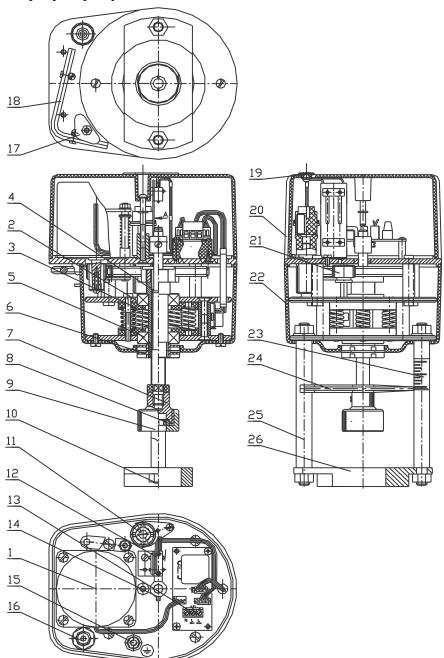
Устройство исполнительного механизма МЭП-1200/ХХ-20-В-Ф-57-35
